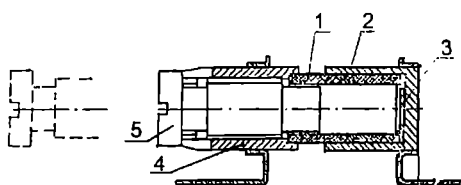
Конструкция цилиндрического подстроечного конденсатора СВЧ-диапазона.
